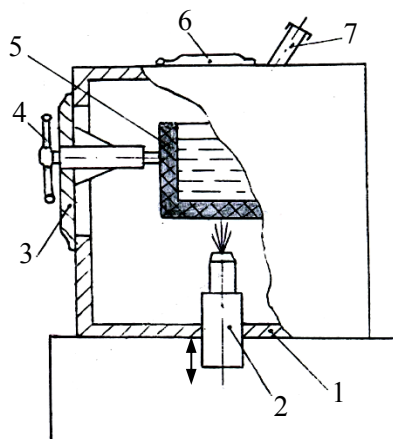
Печь для плавки сплавов путем косвенного нагрева металла плазмой:
